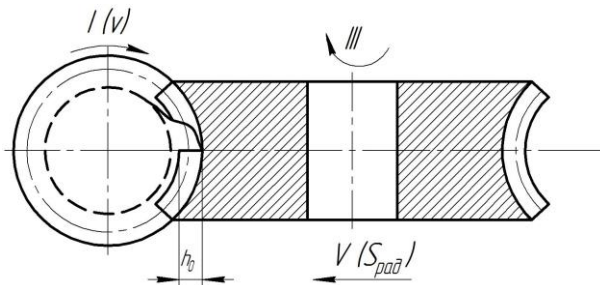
Схема установки специальной фрезы при нарезании червячного колеса
